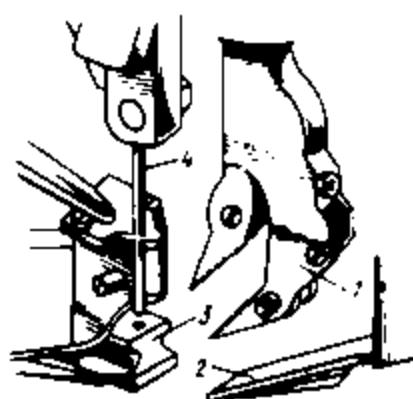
Схема исполнительных механизмов затяжки машины ЗВ-2-О: 1 - клещи; 2 - стельчный упор; 3 - боковой упор; 4 - молоток
